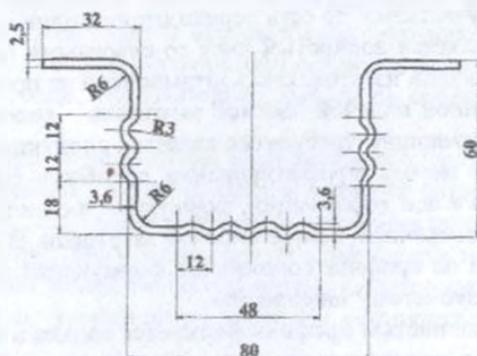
Корытный профиль 80×60×32×2,5 мм.
